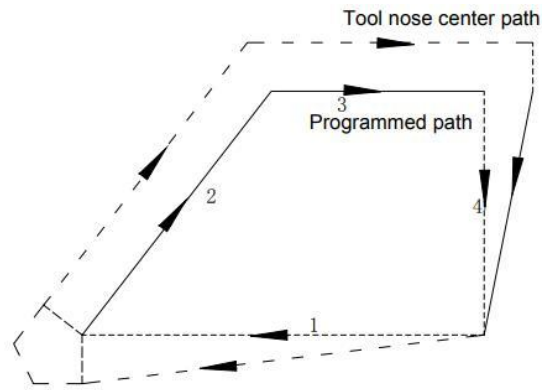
Offset direction of G94 tool nose radius compensation
